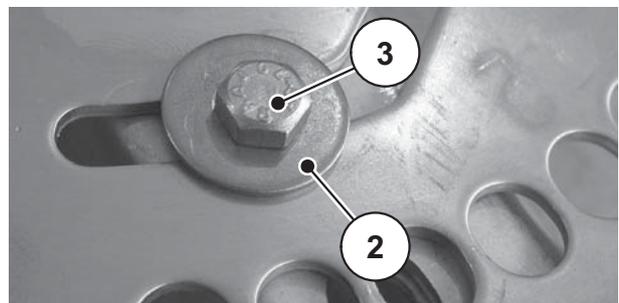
Точки крепления лопаток для разбрасывания
